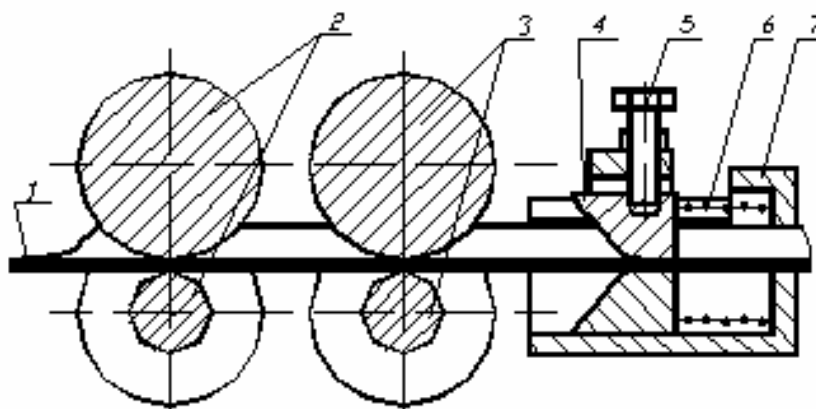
Схема реализации переднего подпора: 1 – заготовка; 2,3 – формирующие ролики двух последних переходов; 4 – фильера; 5 – нажимной винт; 6 – тарированная пружина; 7 – корпус устройства
